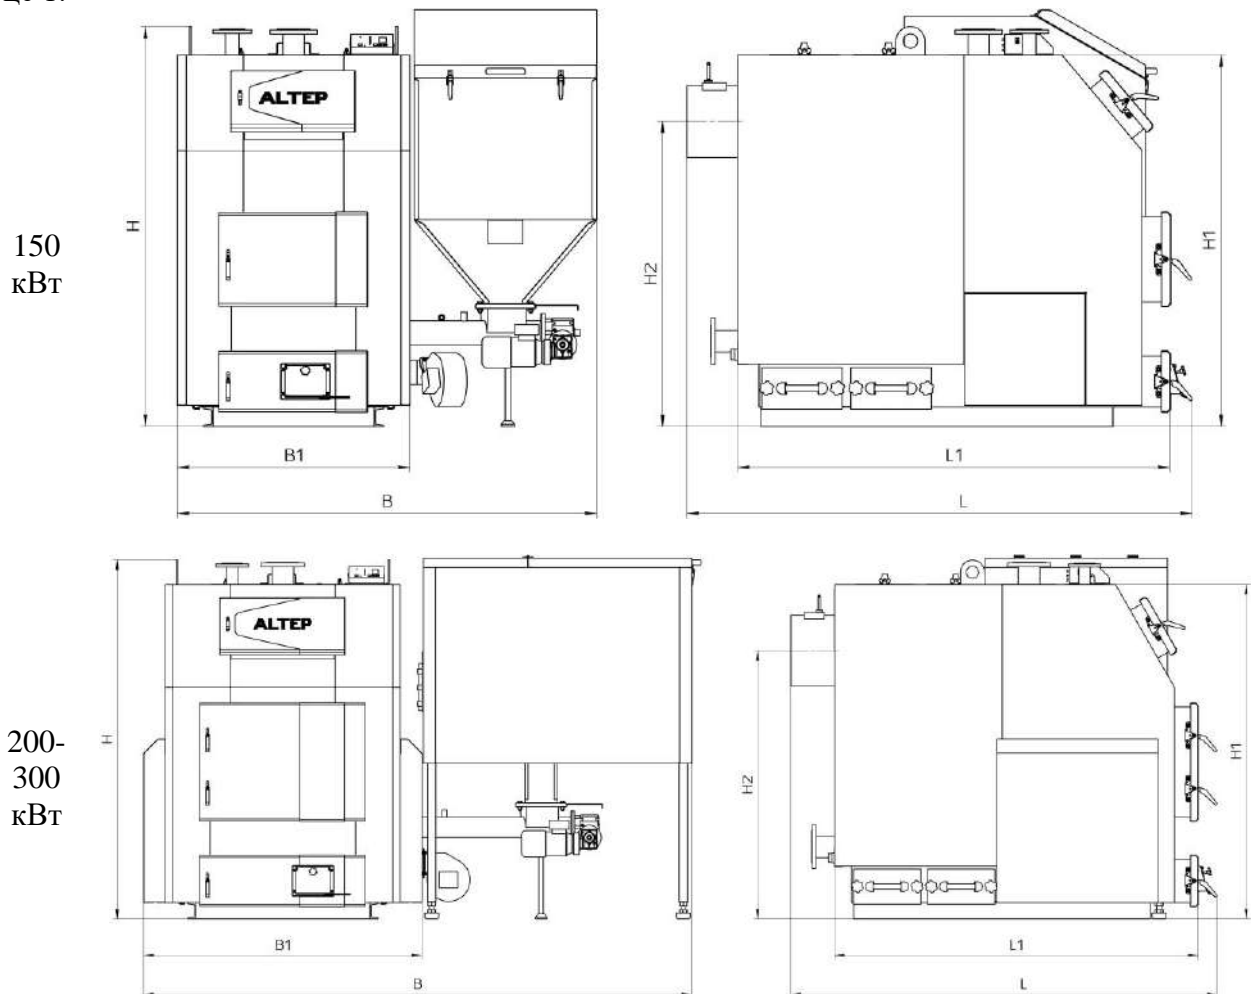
Габаритный чертеж котла типа КТ-3Е-SH
